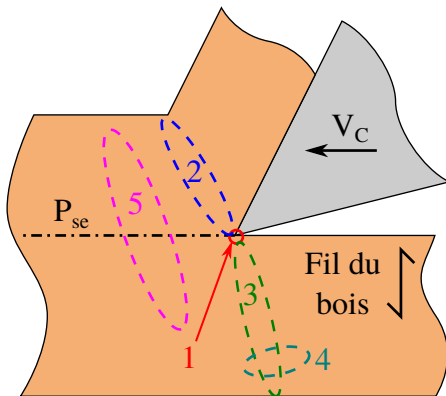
Zones de fissuration lors de la coupe en mode 90-90 (D'après [McKenzie 62]).
